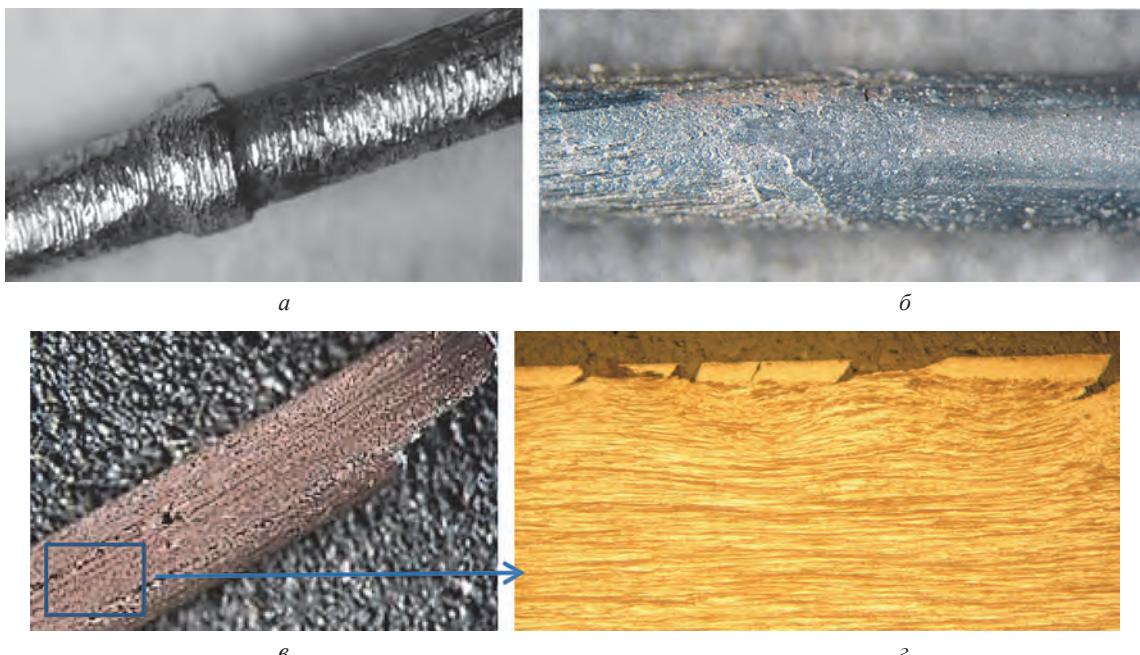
Внешний вид проволоки с некачественной зачисткой сварного шва (*а, б*), вид и микроструктура обрыва проволоки по причине некачественной зачистки сварного шва (*в, г*): *а* – чрезмерная зачистка; *б* – недостаточно зачищена, остатки окалины; *в* – разволоченные поверхностные трещины; *г* – поверхностные трещины по структуре мартенсита истирания (травление в реактиве «Нитал»)
